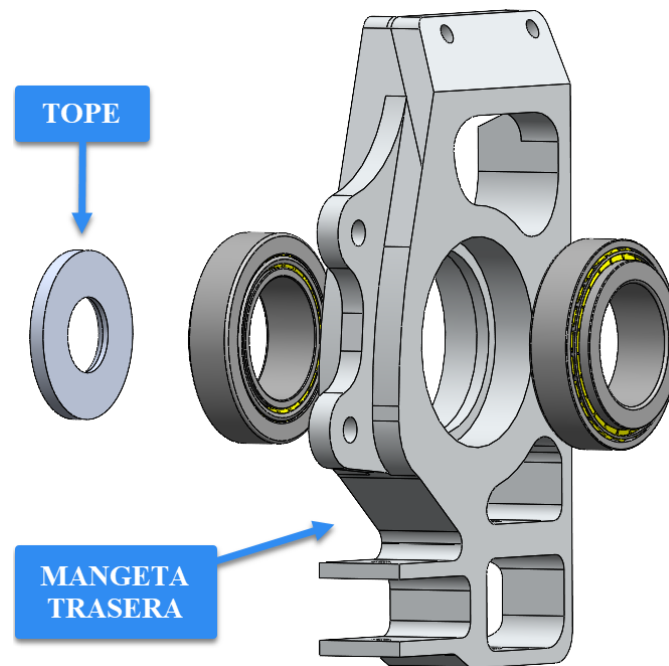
Explosionado conjunto mangueta. Elaboración propia.
